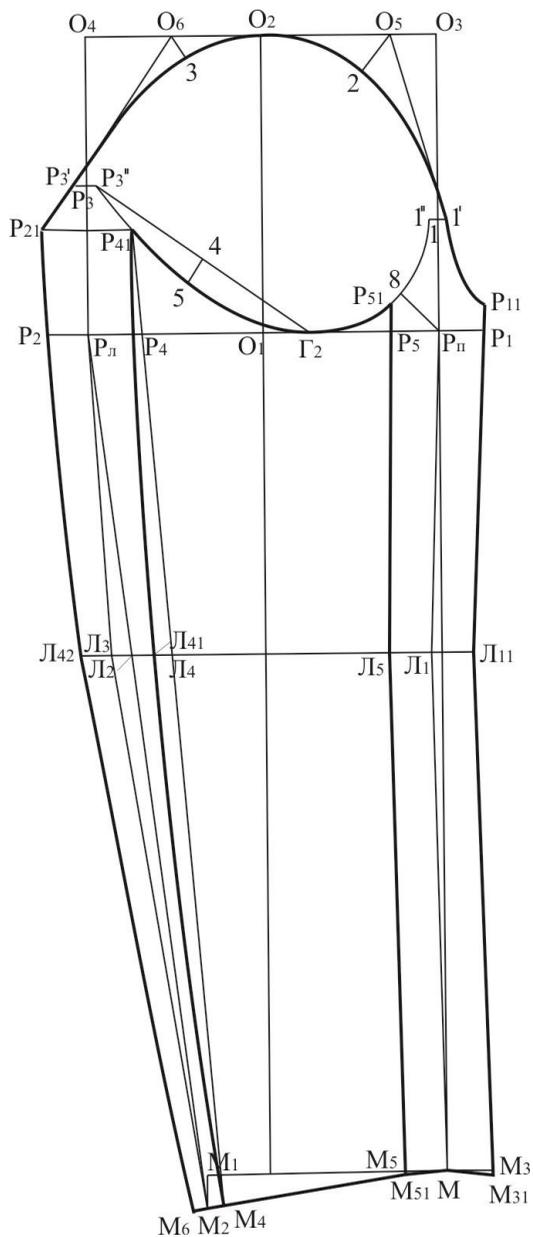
Чертеж конструкции втачного двухшовного рукава
